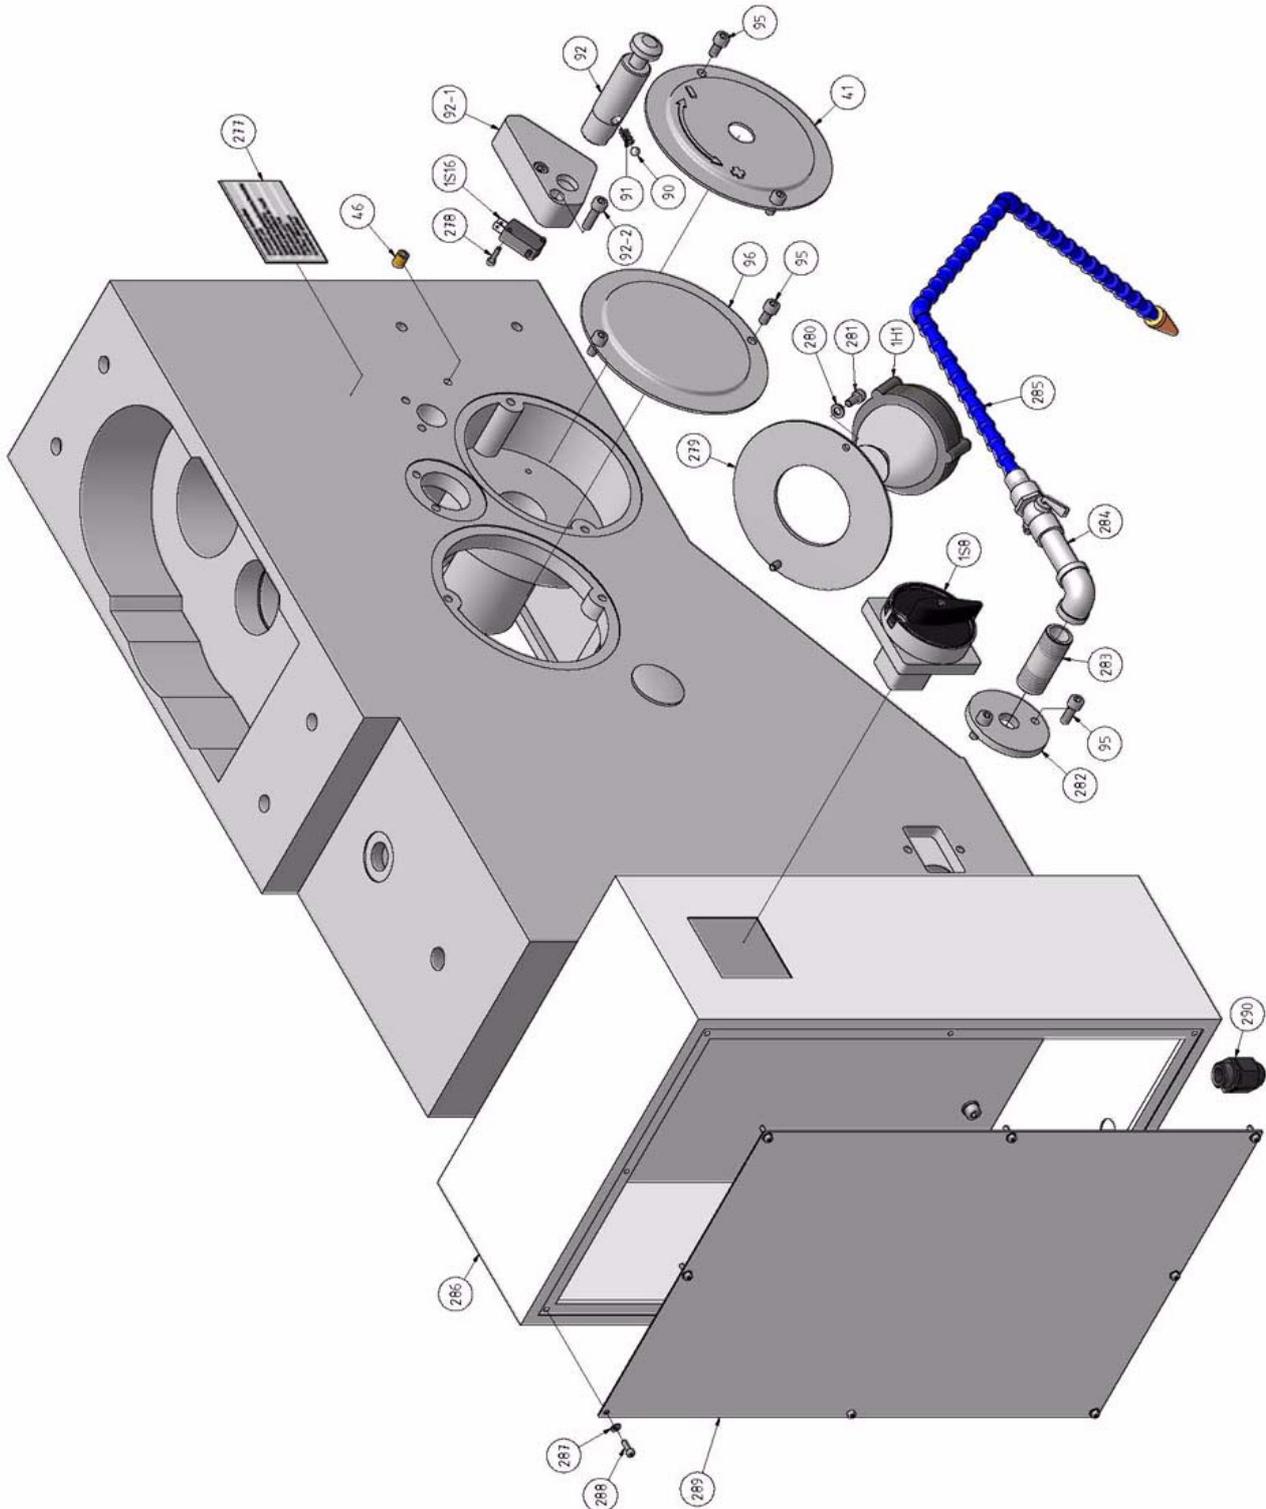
Vorschubgetriebe 4 von 4 - Feed gear box 4 of 4
